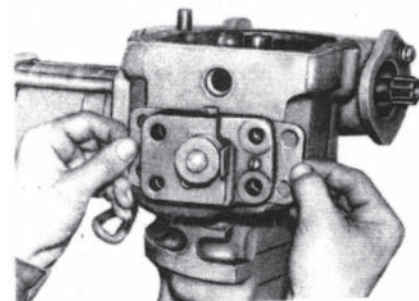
Установка регулировочных прокладок под фланец датчика блокировки дифференциала
